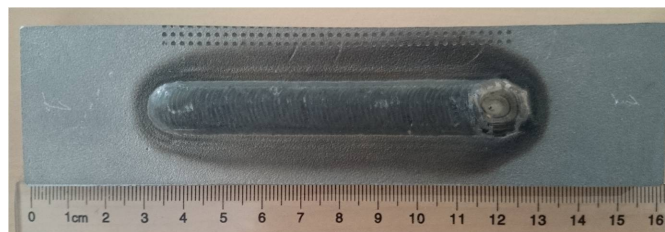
Plaque soudée utilisée pour le choc laser
